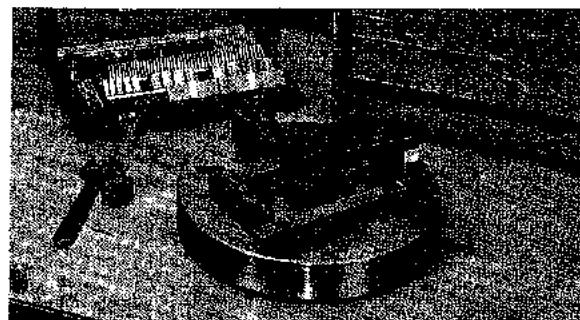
Colocación y sujeción de la pieza encima del plato frontal (South Bend Lathe Works).
